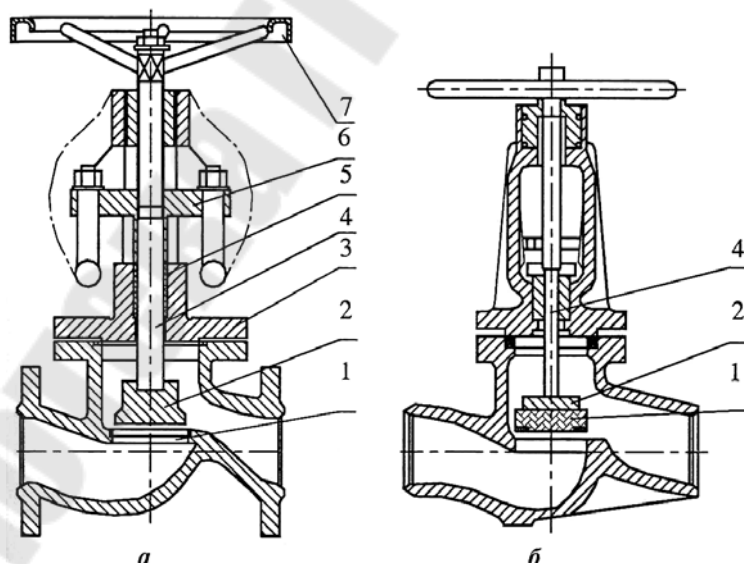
Запорные вентили: а - ранцевый, тип 15ч14бр; б - приварной, тип 15с65бк; 1 — уплотнительная поверхность, 2 - затвор, 3 - крышка, 4 - шпindel, 5 - уплотнение, 6 - втулка, 7 — маховик
